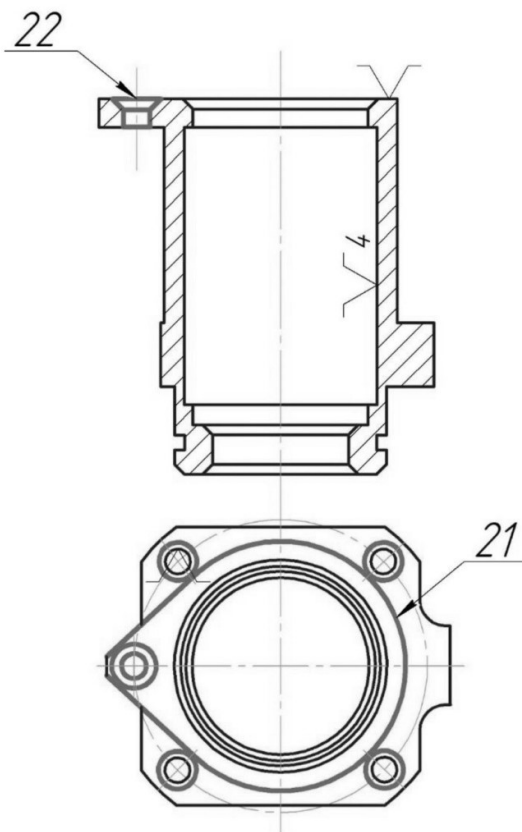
Ескіз для фрезерної операції з ЧПК
